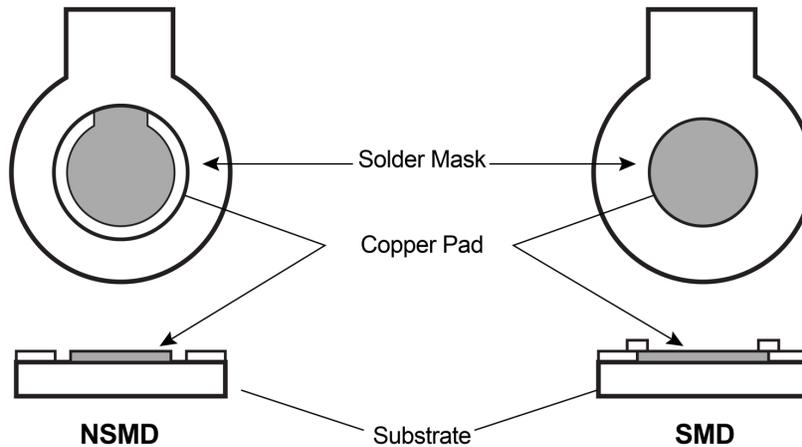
NSMD 和 SMD PCB 焊盤模式
